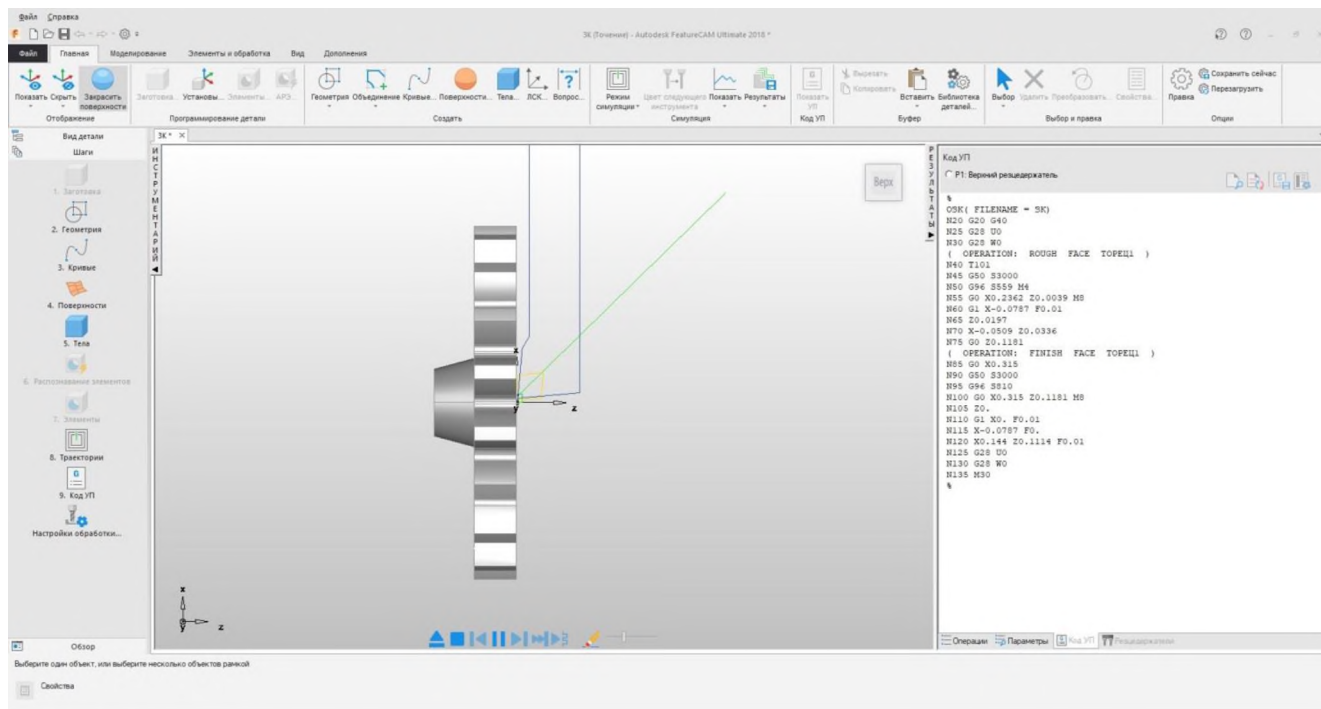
Підбір металорізального інструмент для обробки
